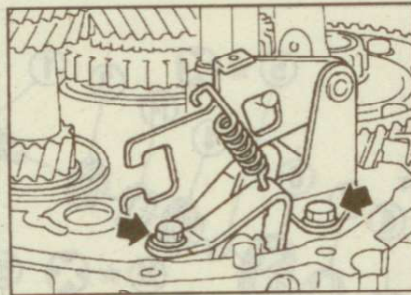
Расположение болтов крепления рычага передачи заднего хода
